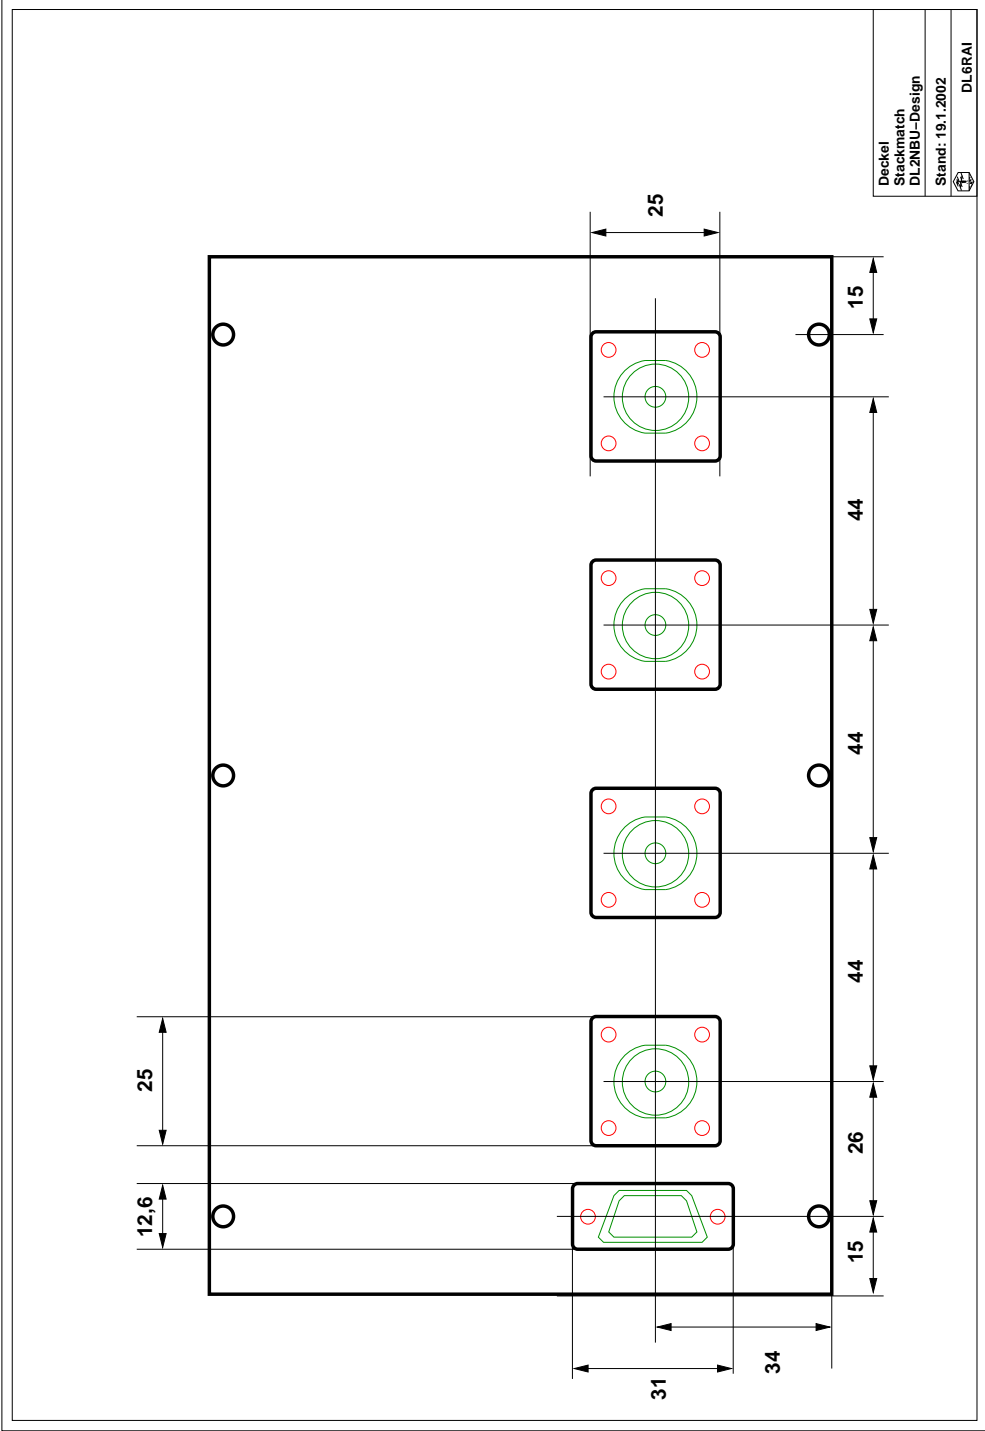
Bemaßungen für die Bohrungen im Gehäusedeckel.
